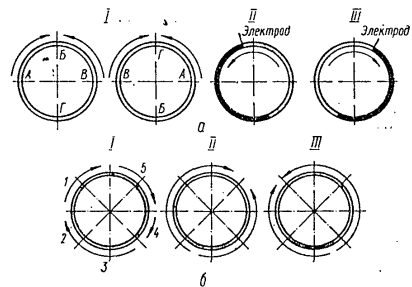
Последовательность выполнения ручной электродуговой сварки:
